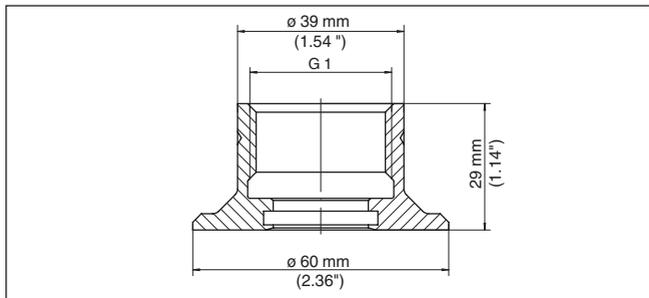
didas da luva para soldagem G1 (DIN 3852-X)
